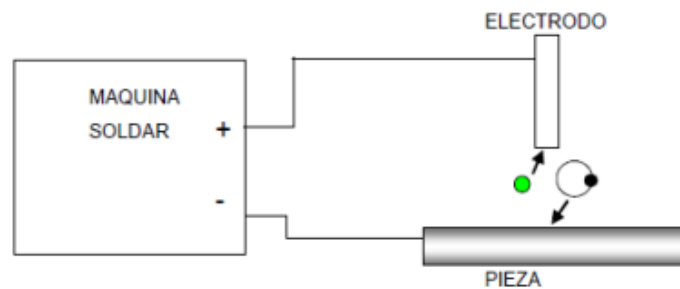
Esquema de Polaridad Inversa de la Soldadora GTAW.
